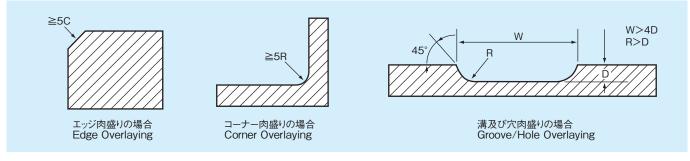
肉盛り溶接における標準開先形状 Figure 1. Standard groove shapes for overlay welding
